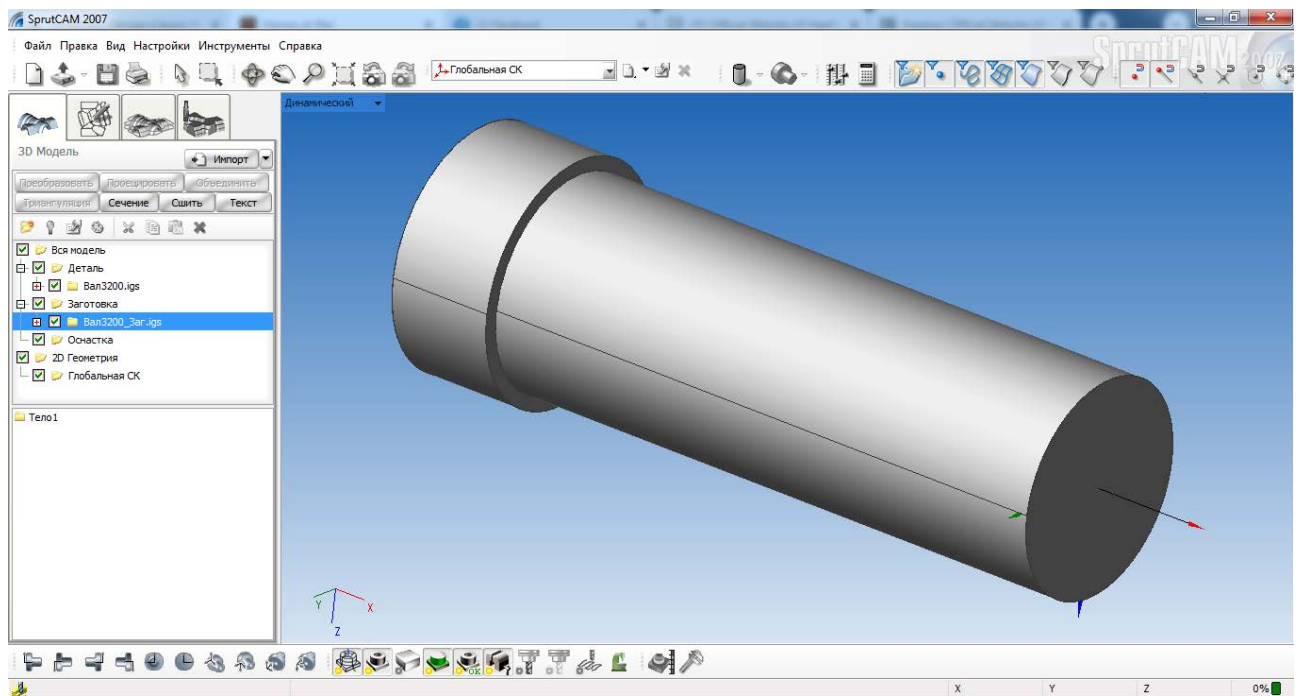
3D-модель заготовки вала, імпортована у систему SprutCAM
